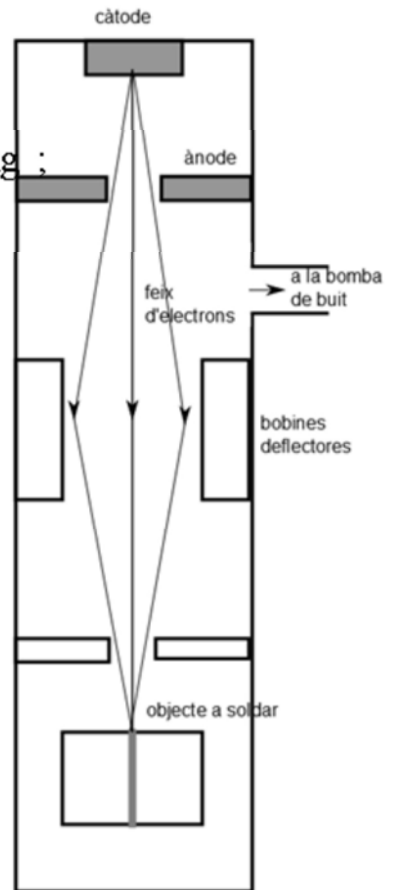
Dispositiu de soldadura per feix d'electrons
